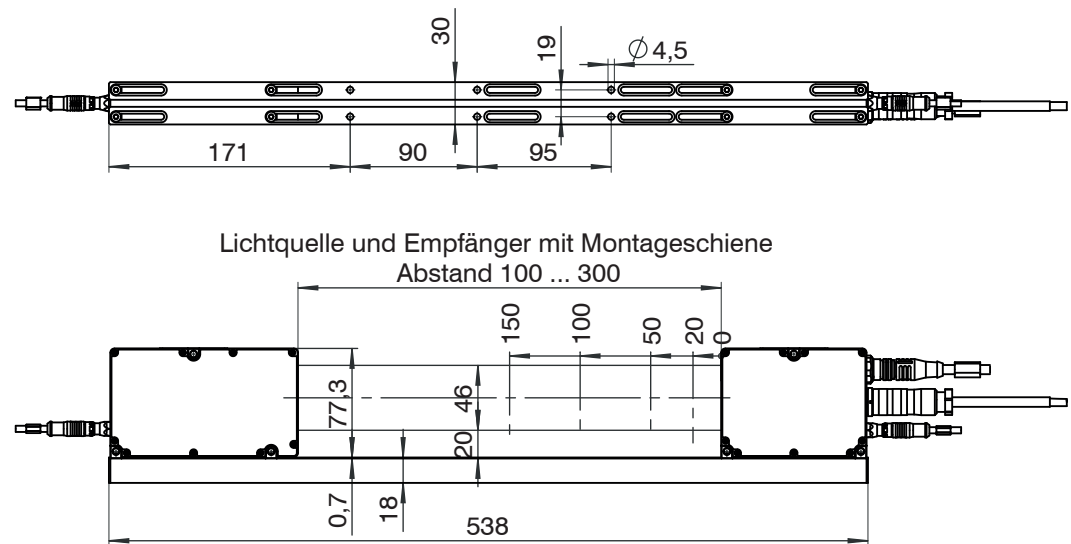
Lichtquelle und Empfänger optoCONTROL 2520-46 mit Montagesschiene, Abmessungen in mm
